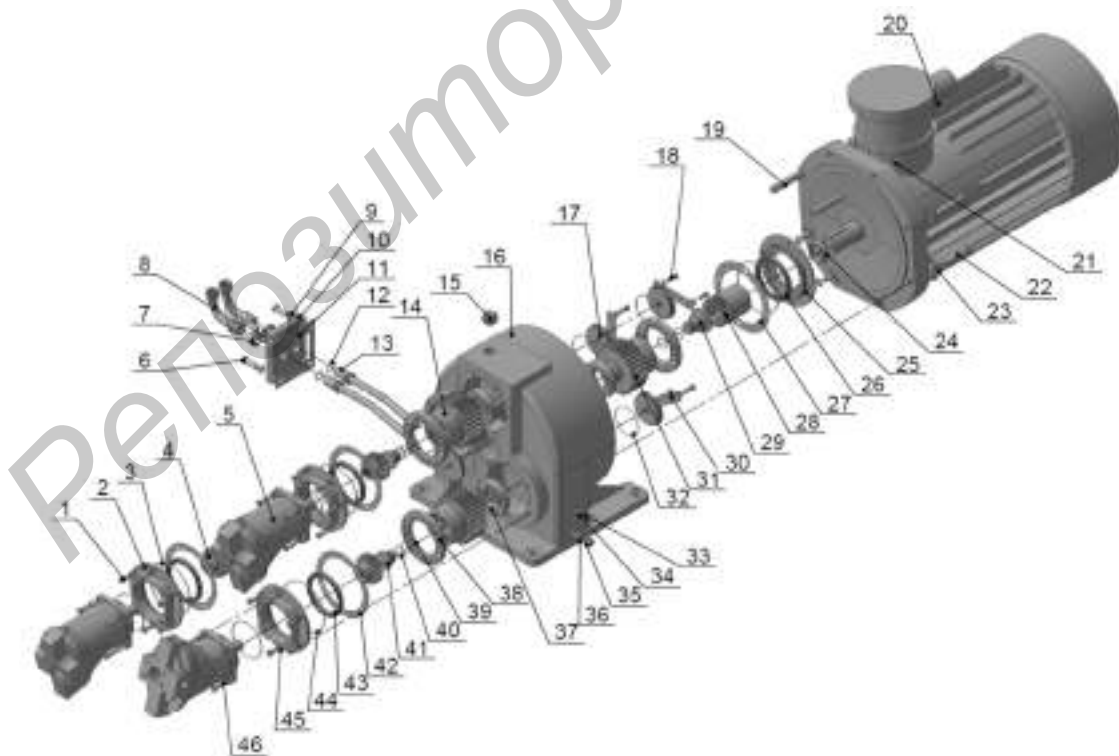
Состав насосной установки: 1, 6, 18, 22, 46 — болты, 2 — проставка; 13 — теплообменник; 8 — трубопровод; 17 — крышка; 16 — корпус; 15 — сапун; 14 — шестерня, направление зуба левое; 31 — шестерня, направление зуба правое; 4, 28 — полумуфта; 25 — крышка; 29, 41 — заглушка; 27, 39, 42 — прокладка; 24 — кольцо; 19 — шпилька; 21 — гайка; 11 — прокладка; 30 — планка; 10 — крышка; 7 — гайка; 3, 12, 32, 40, 44 — кольца; 43 — манжета; 37, 38 — подшпильники; 9, 23, 45 — шайбы; 33, 35 — пробки; 34, 36 — прокладки; 20 — двигатель; 5 — насос; 26 — манжета
